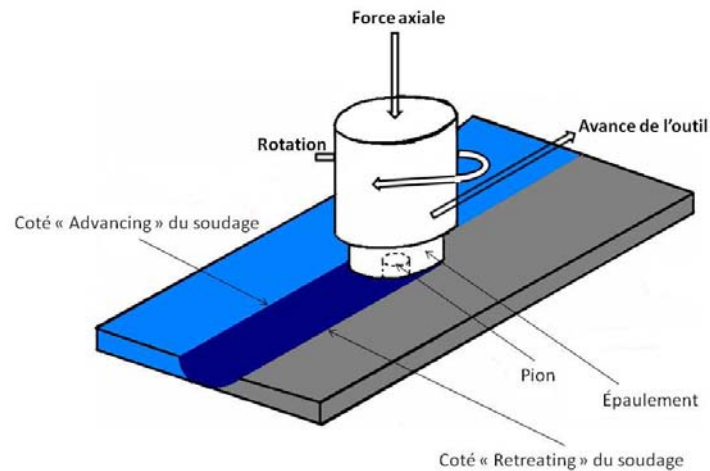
Illustration du procédé de soudage par friction et malaxage
